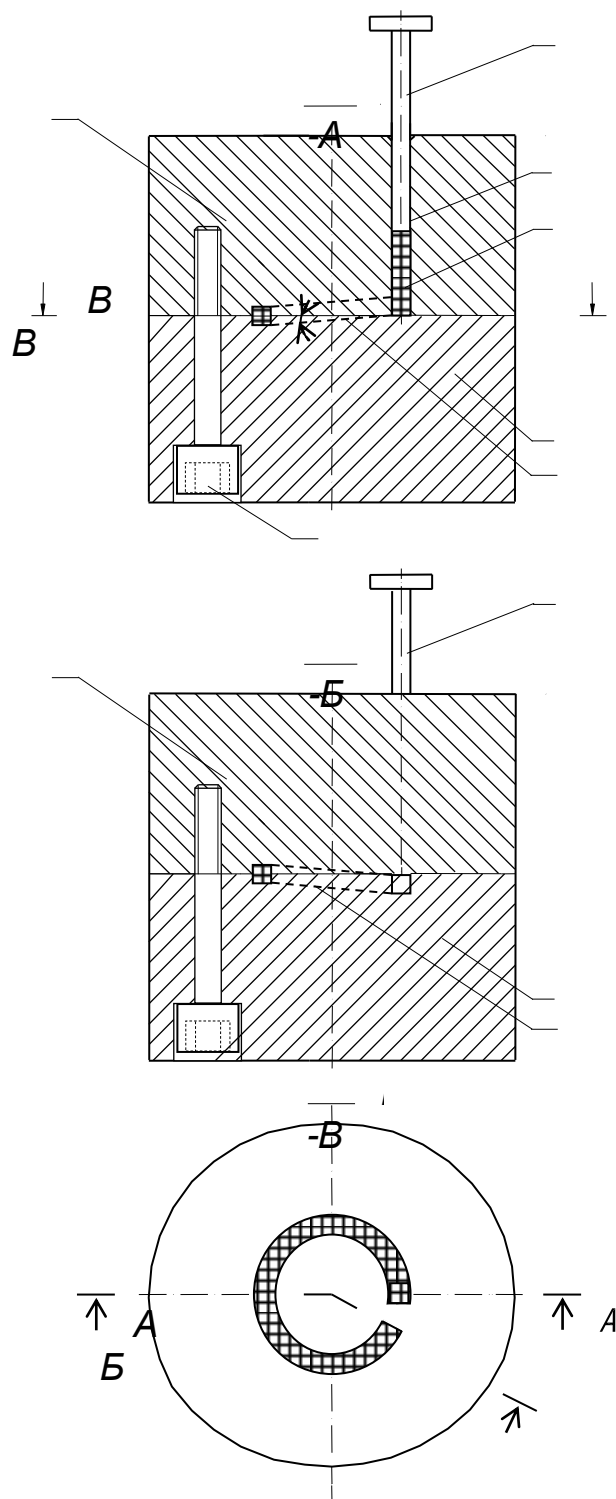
Схема устройства для РКУП призматической заготовки (1 и 2 – верхняя и нижняя полуматрицы, соответственно, 3 – вертикальный канал, 4 – заготовка, 5 – пуансон, 6 – канал, 7 – винт).
